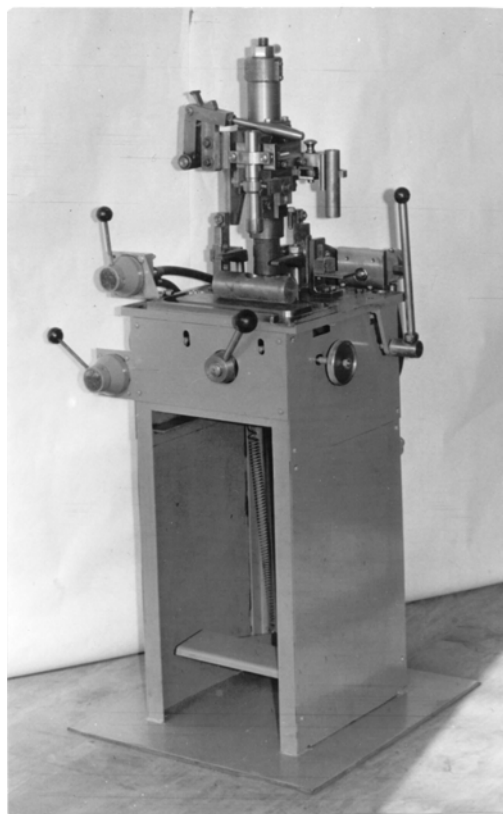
Установка для збирання деталей заготовок трійників під паяння із широким зазором
